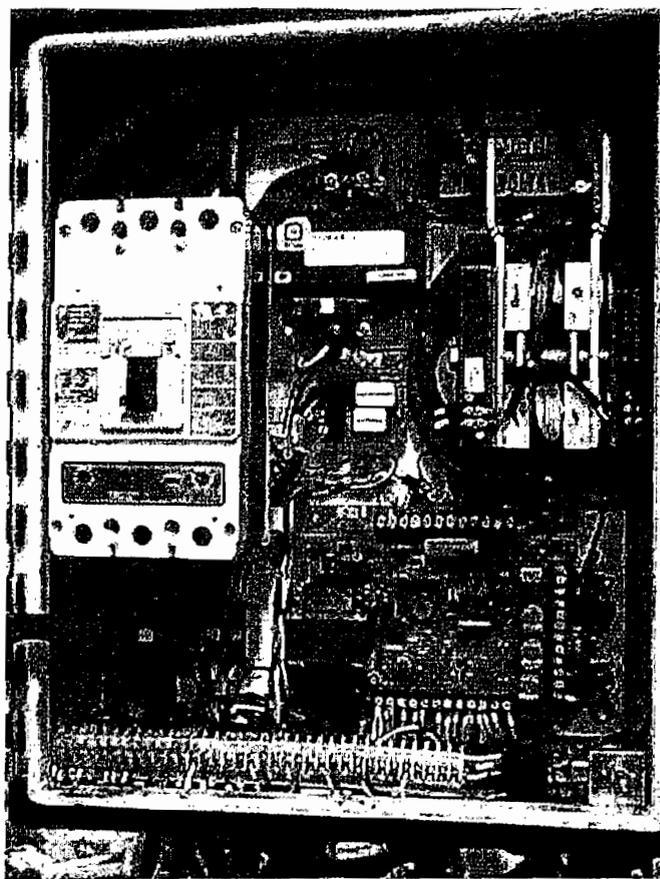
B) TABLERO INTERNO DE LA MÁQUINA SOLDADORA MEDAR MIZ'R
